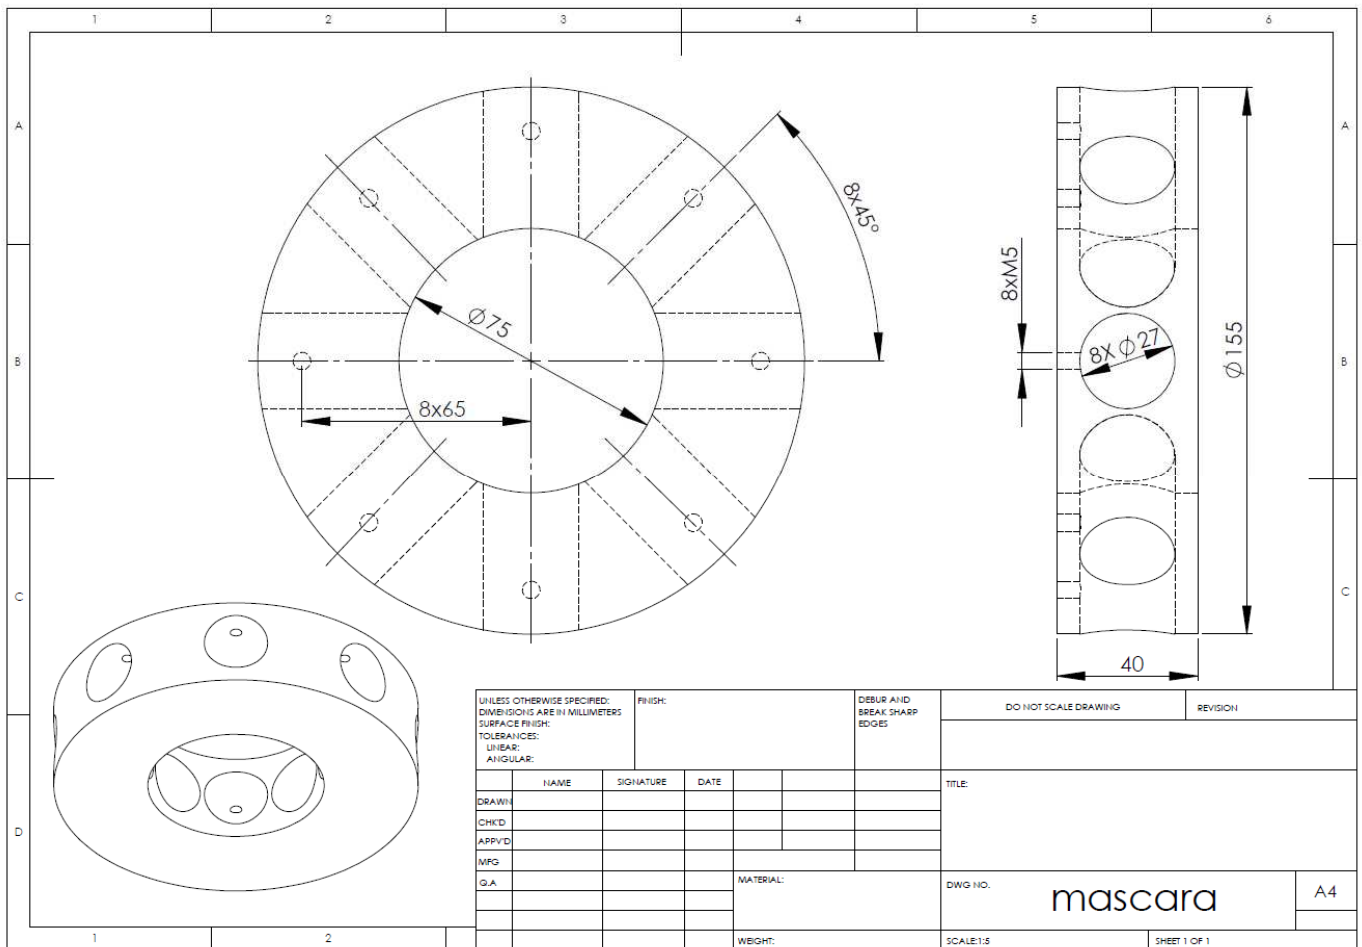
Desenho técnico para o suporte das bobinas excitadoras do sistema BAC Circular (Mascara).
